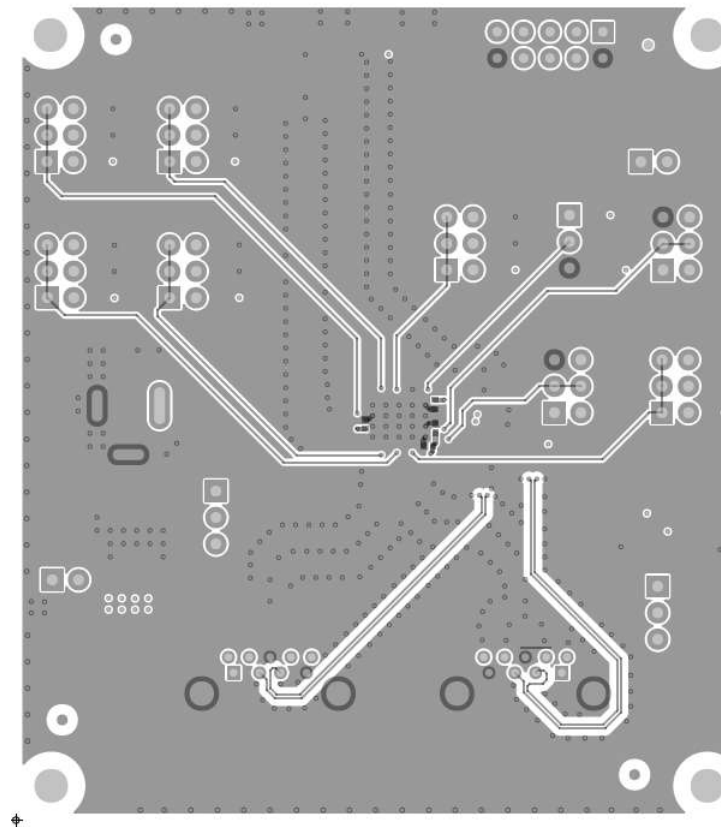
TUSB521Q1-EVM PCB 第 6 层 ( 底部 )
